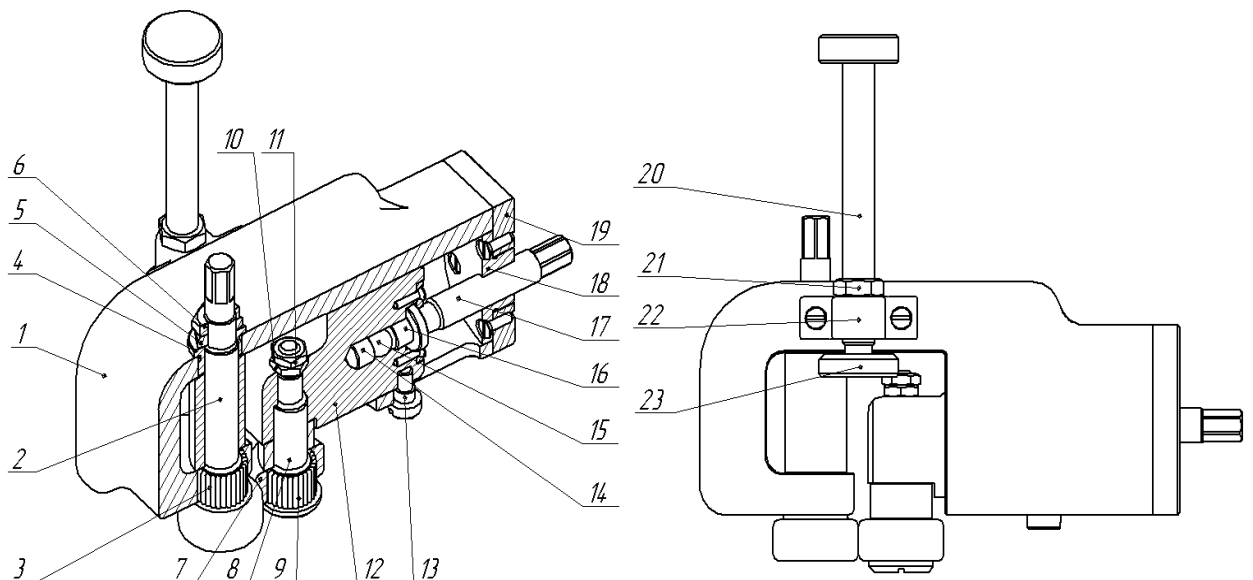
Конструкция раскатника для обработки ребер
